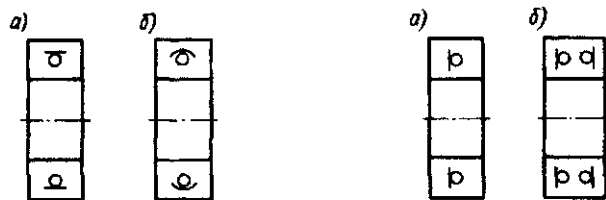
Шариковый подшипник радиальный: *а* — однорядный; *б* — самоустанавливающийся (сферический)
